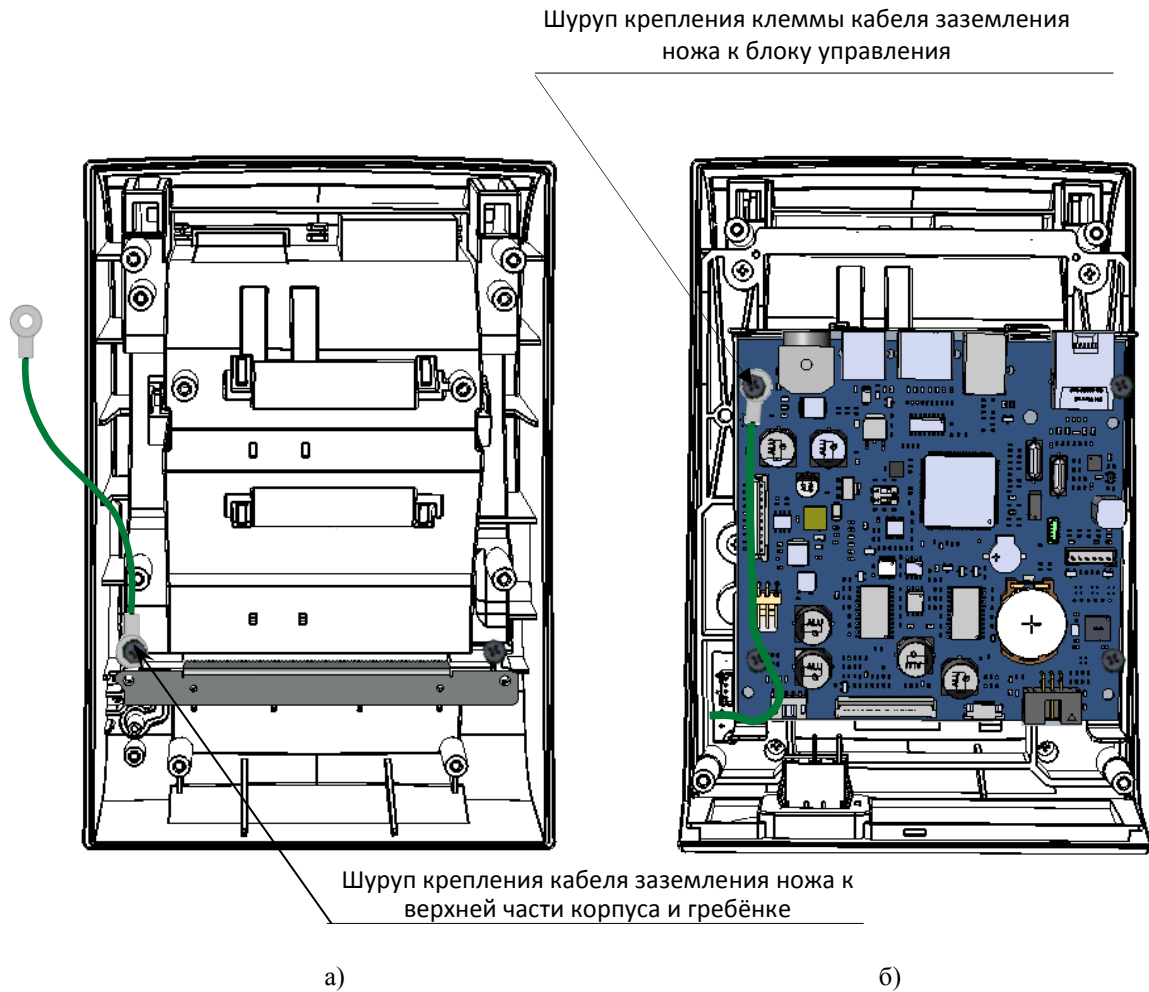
Установка кабеля заземления ножа: а) крепление в верхней части корпуса ККТ; б) крепление к блоку управления
